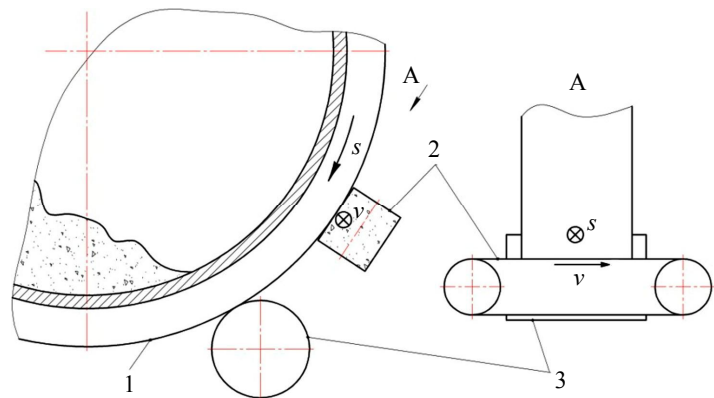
Схема ленточного шлифования бандажа на вращающейся печи
